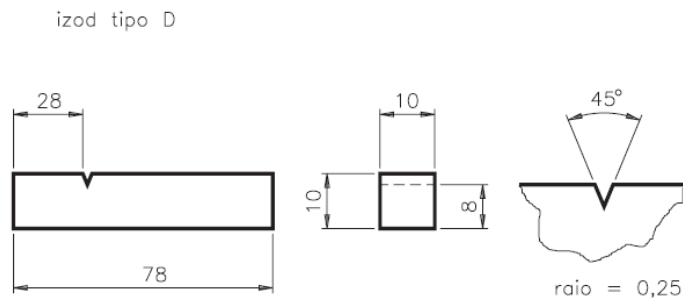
Corpo de prova para ensaios Izod (dimensões em milímetros) [59].
